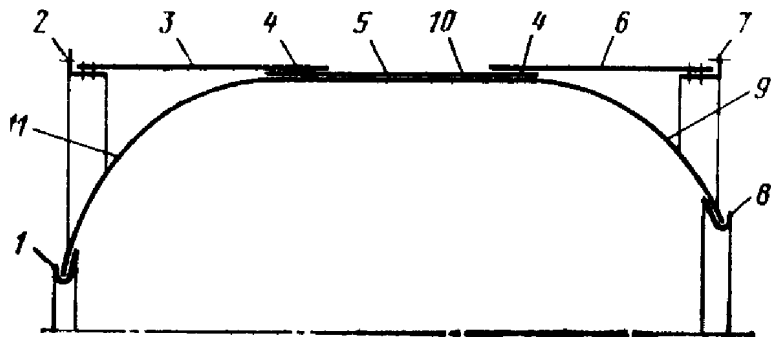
Конструктивная схема корпуса РДТТ из композиционного материала: 1 - передний стыковочный фланец; 2 - передний шпангоут; 3 - передний узел стыка; 4 - зона соединения (намотки) узлов стыка с силовой оболочкой; 5 - кольцевые слои силовой оболочки; 6 - задний стыковочный узел; 7 - задний шпангоут; 8 – задний (сопловой) стыковочный фланец; 9 - заднее днище силовой оболочки; 10 - цилиндрическая часть силовой оболочки; 11 - переднее днище силовой оболочки
